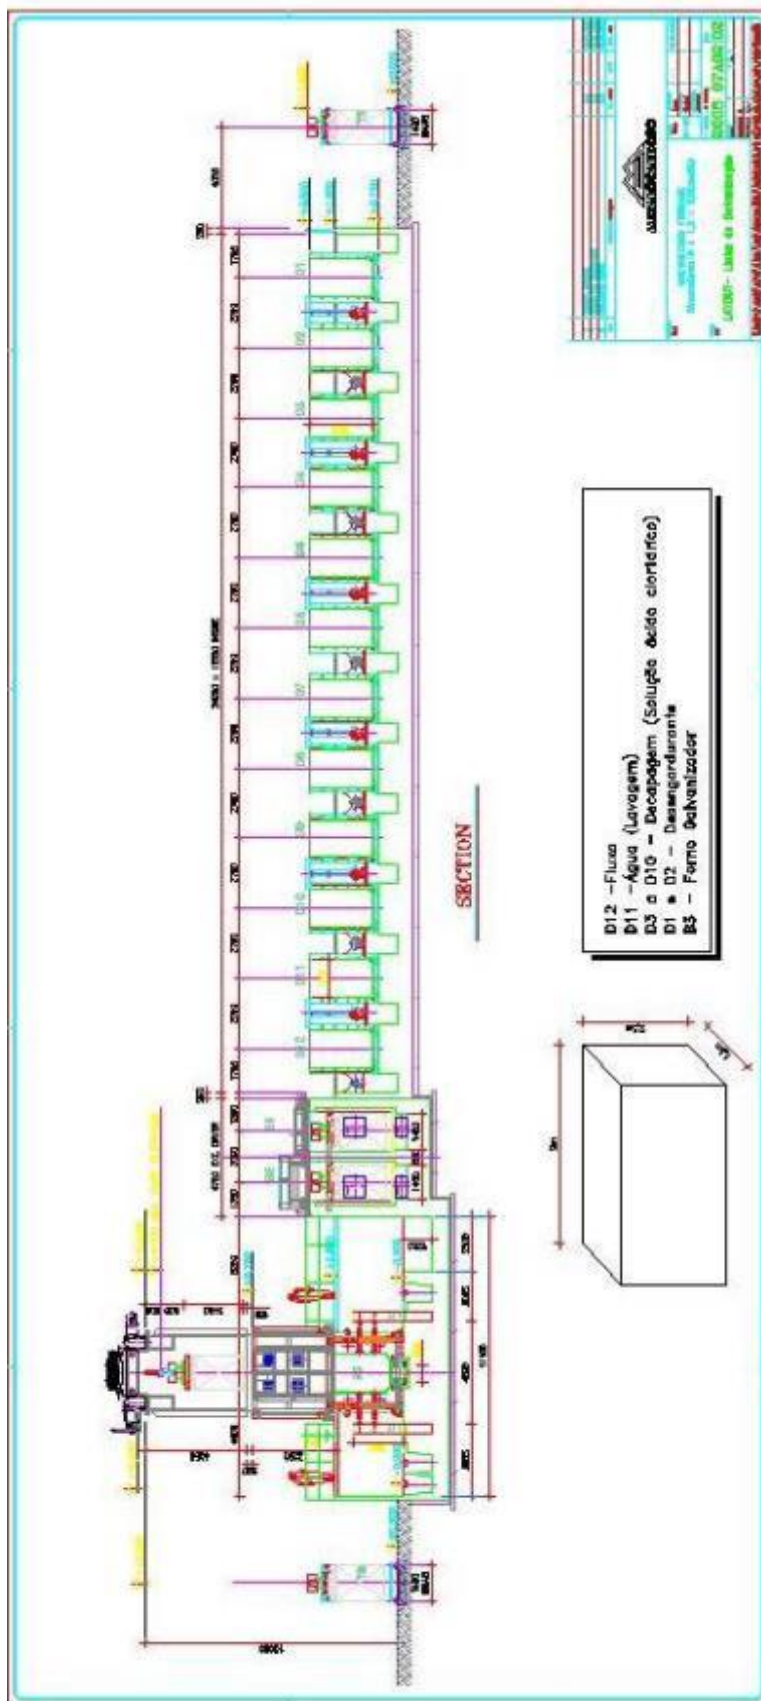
Planta de implantação da linha de galvanização da METALOCARDOSO.
